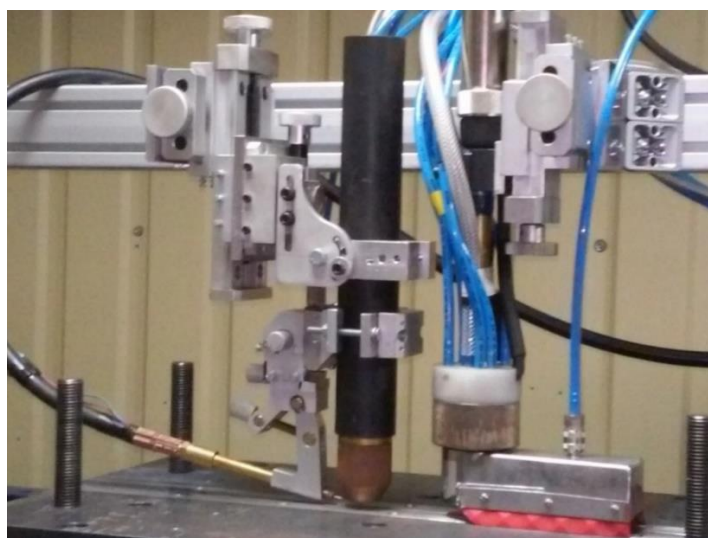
Зовнішній вигляд інструменту для комбінованого зварювання стисненою дугою різнополярного струму та гібридним плазмо-дуговим зварюванням плавким електродом.
